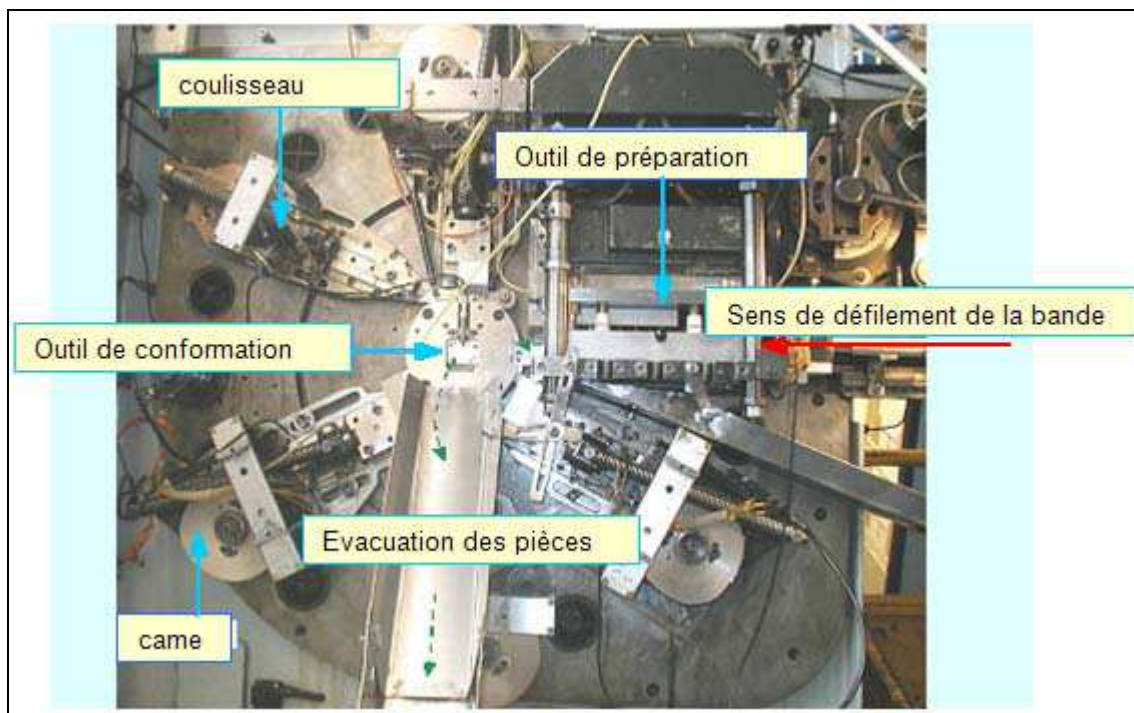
Vue d'ensemble d'un outil sur presse à coulisseaux multiples BIHLER.
